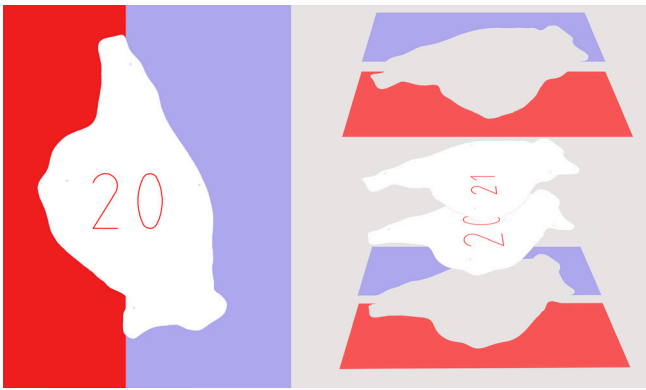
Impresión de la planta necesaria. Las dos zonas de color se corresponden a los dos soportes deslizables que sujetarán la pieza a transportar. Derecha, perfil del recorte de la cara superior e inferior de la plancha elegida. En blanco, silueta superior e inferior de la pieza, áreas desechables quedando el negativo ajustado a la misma.
